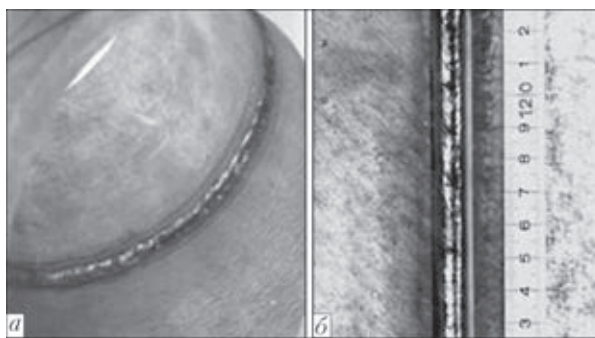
Блестящий гладкий валик на обратной (а) и лицевой (б) поверхности корневого шва (сталь 304, пруток TG-X308L)
